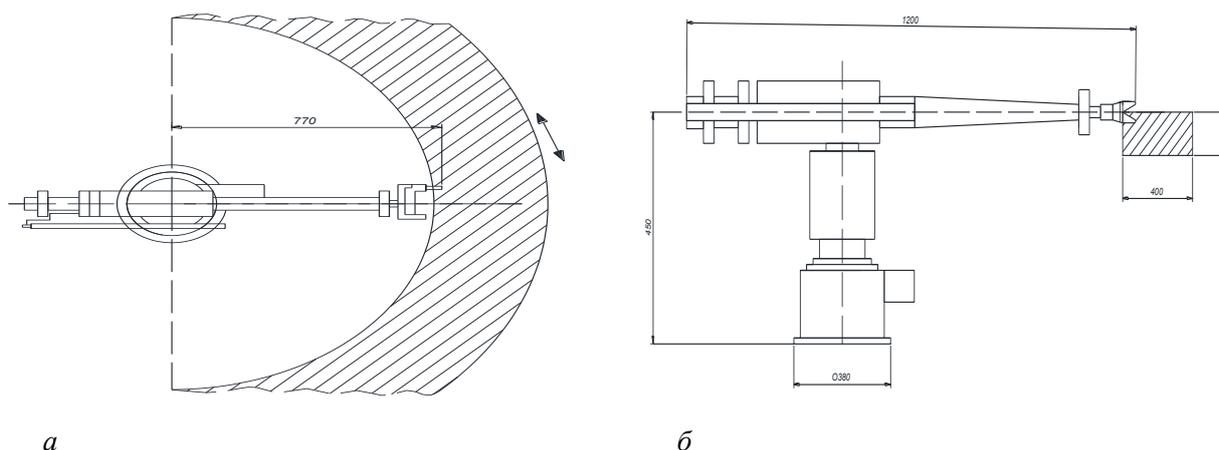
Промышленный робот AISARBT 5: а - вид сверху; б - вид сбоку
